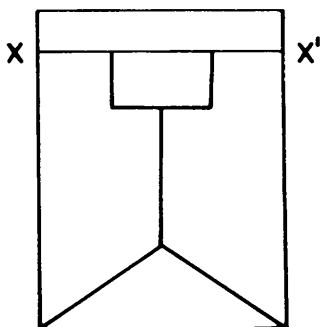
Corte longitudinal do anel de fundição com o padrão de cera incluído em revestimento.
